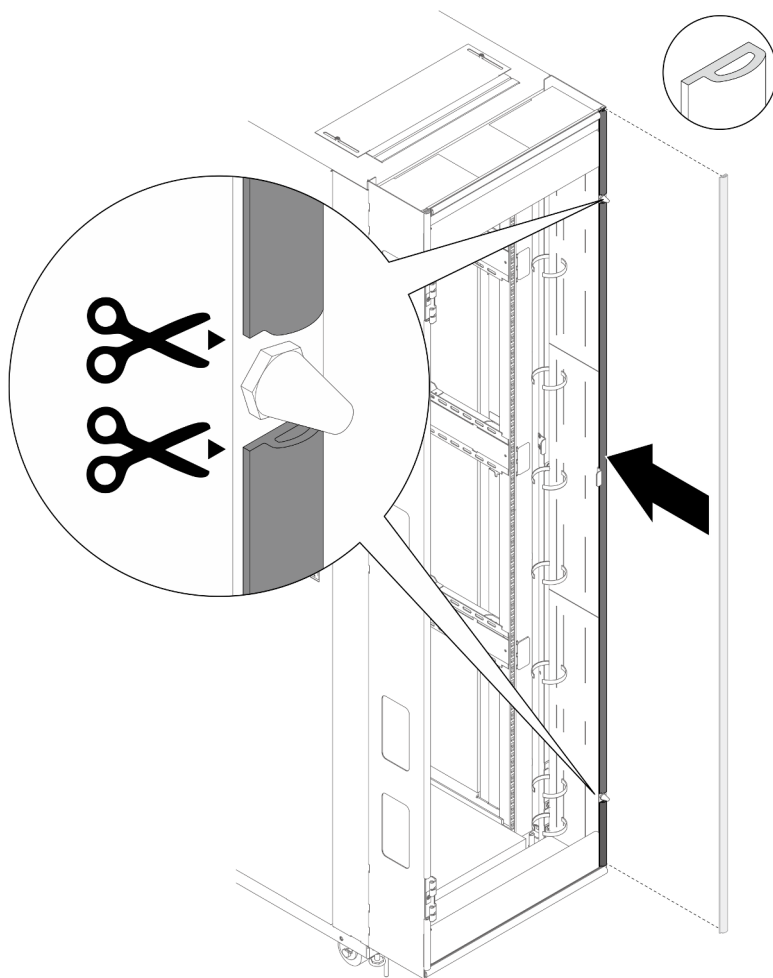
Installation de la mousse d'étanchéité d'extension sur le côté droit de l'armoire
